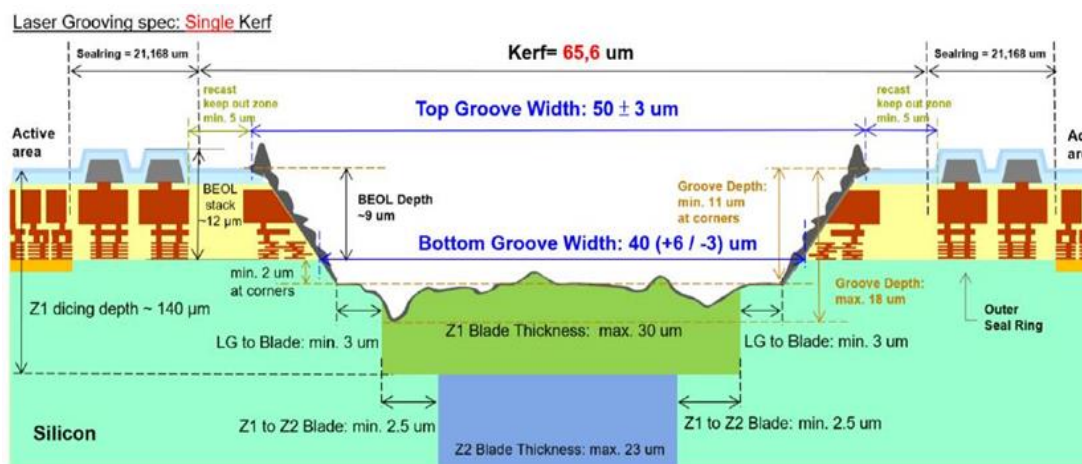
Esquema representativo do corte em laser grooving e blade dicing
